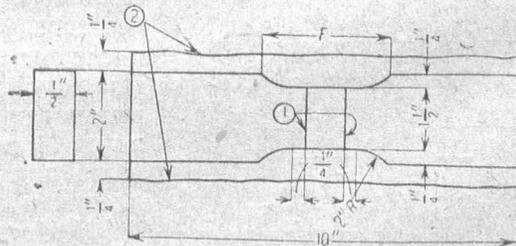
а. Образец для испытания соединения на разрыв. 1 — основание шва; 2 — если образцы вырезаны газом, то эти кромки должны быть обработаны
